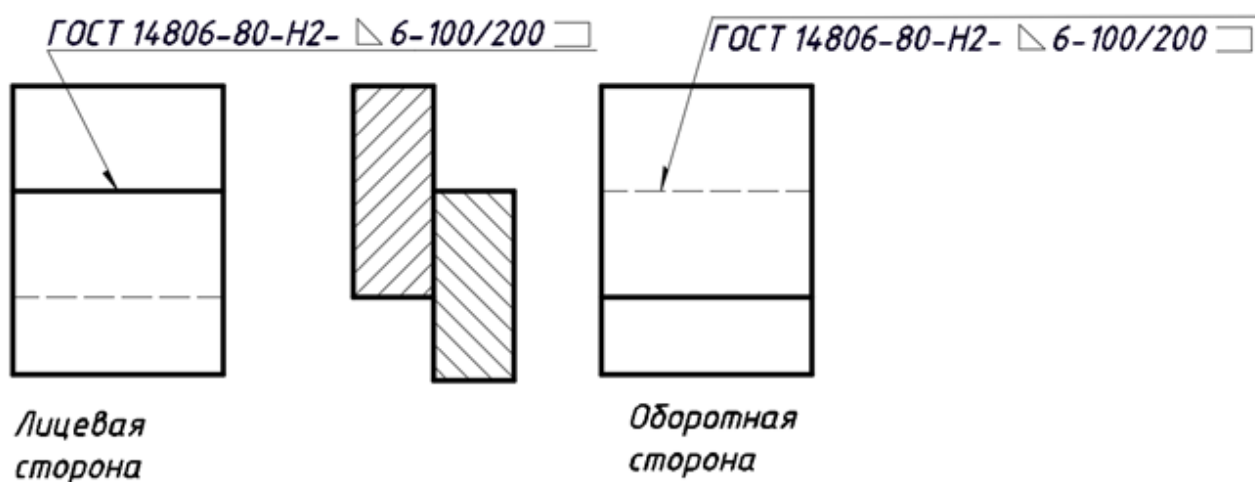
Образец условного обозначения сварного шва.
